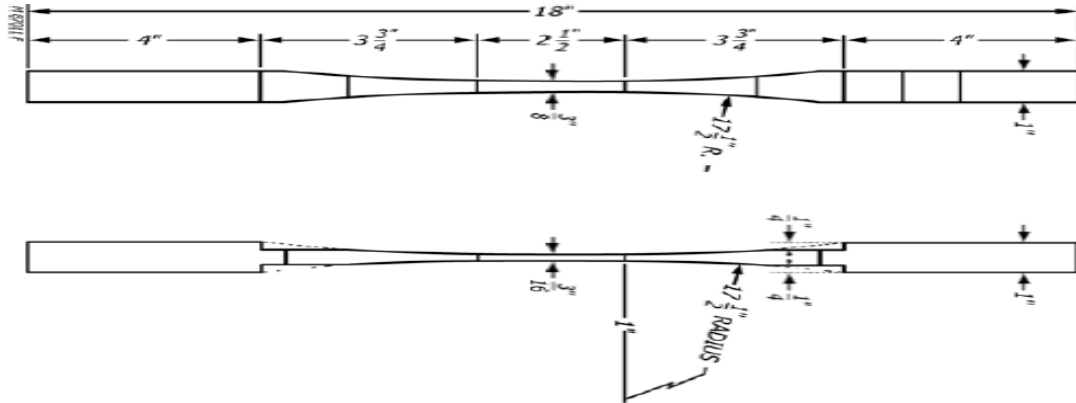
Dimensiones de la probeta para ensayos de tensión.
